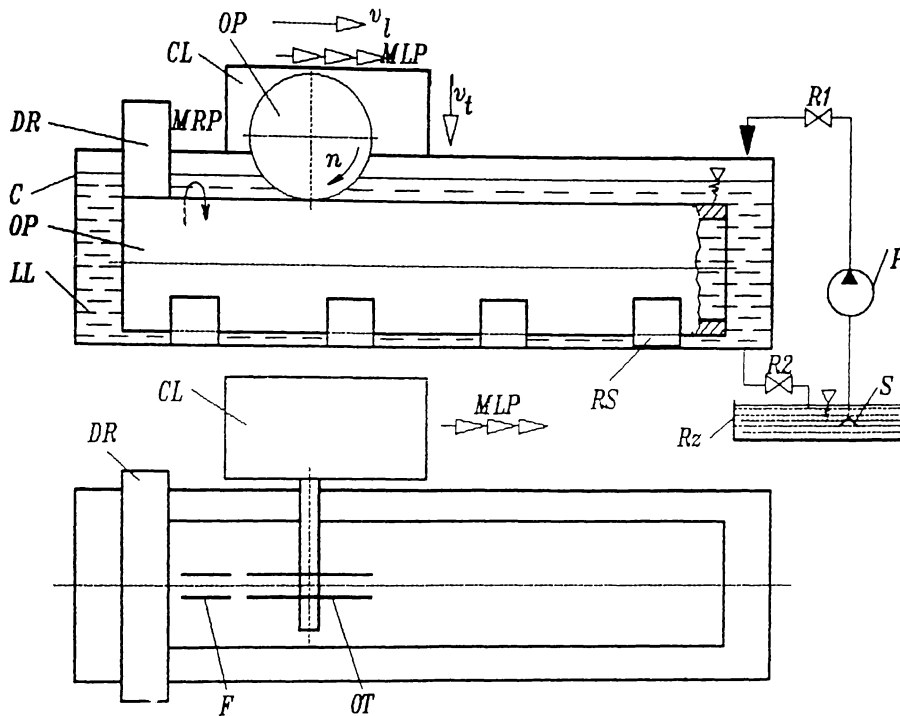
Schema mașinii de prelucrare a fantelor prin EEC în semifabricate tubulare
